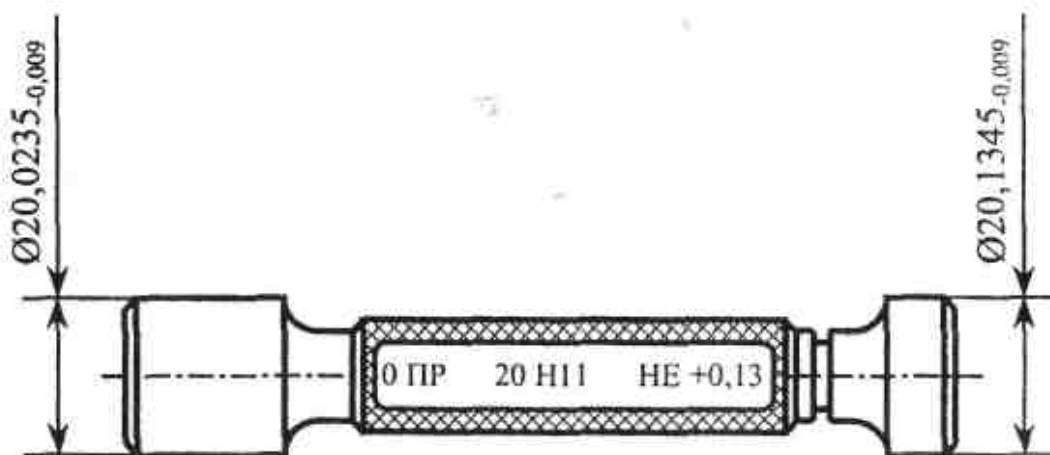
Маркировка и обозначения исполнительных размеров калибр – пробки.
